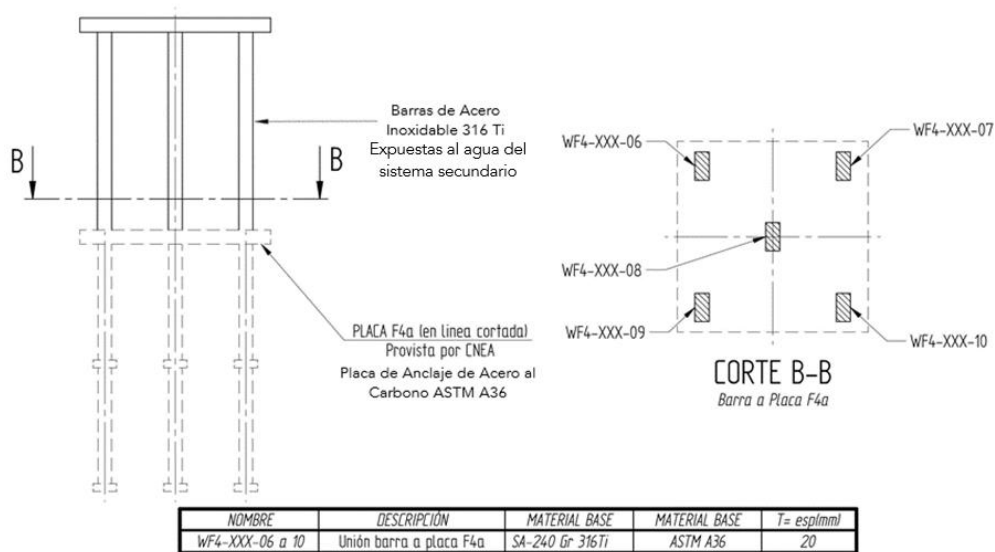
Se detallan las soldaduras entre las barras de unión de Acero Inoxidable AISI 316Ti y la placa de anclaje de Acero al Carbono ASTM A36.
